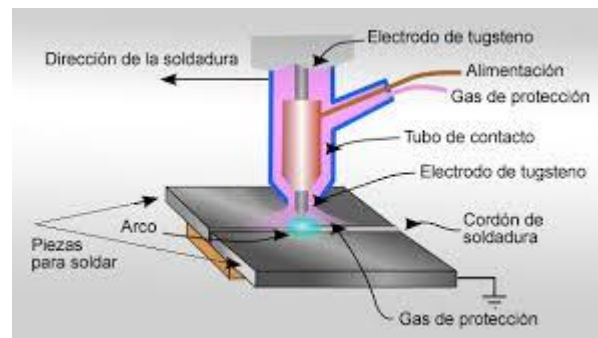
Soldadura de aluminio. Fuente: *escueladesoldadores.com* (2016)
